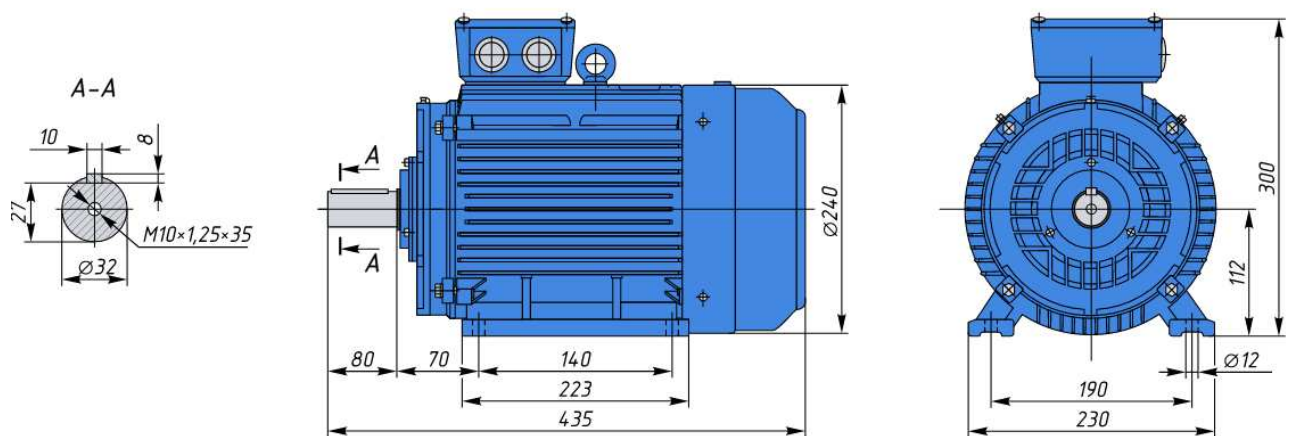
Габаритні та установочні розміри приводного двигуна
